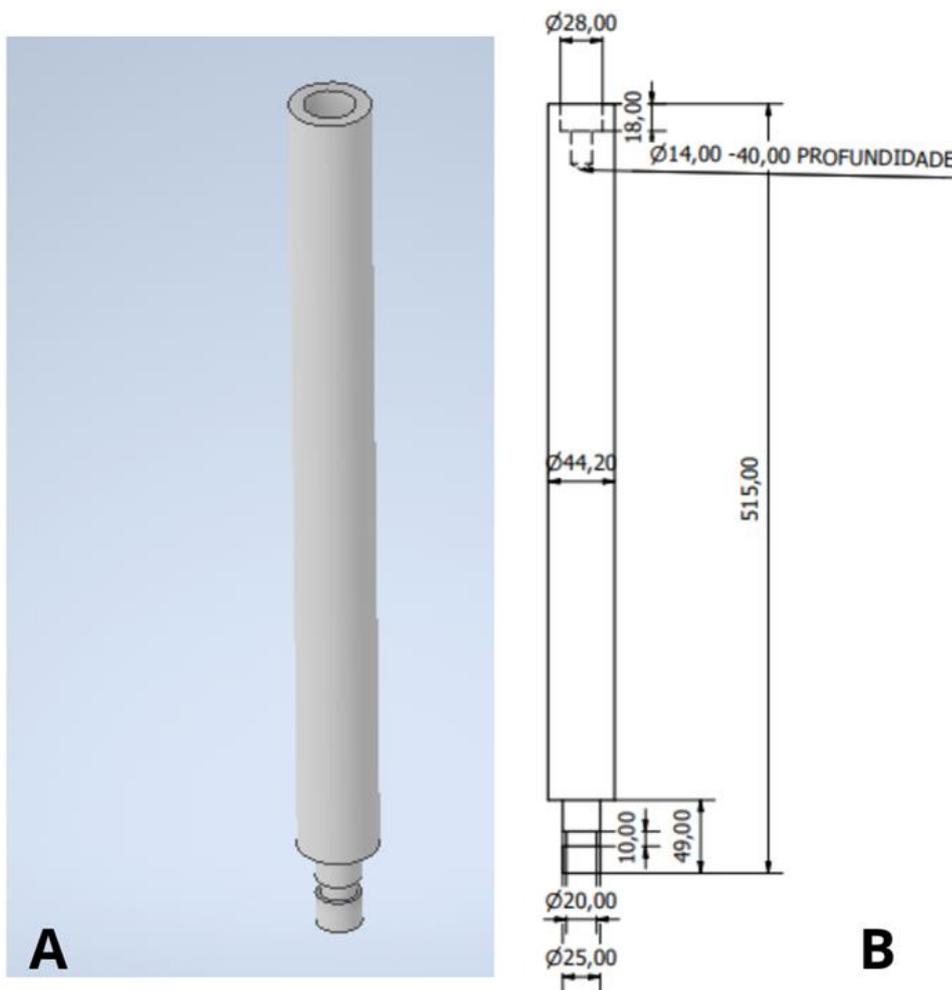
(A) Desenho 3D do extrator; (B) Desenho 2D do extrator.
